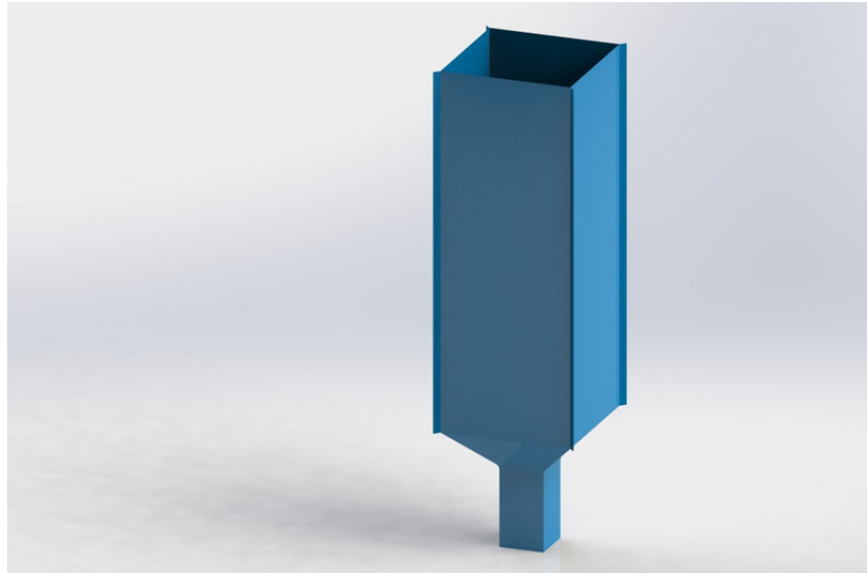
Bolsa con soldadura en las aristas.
